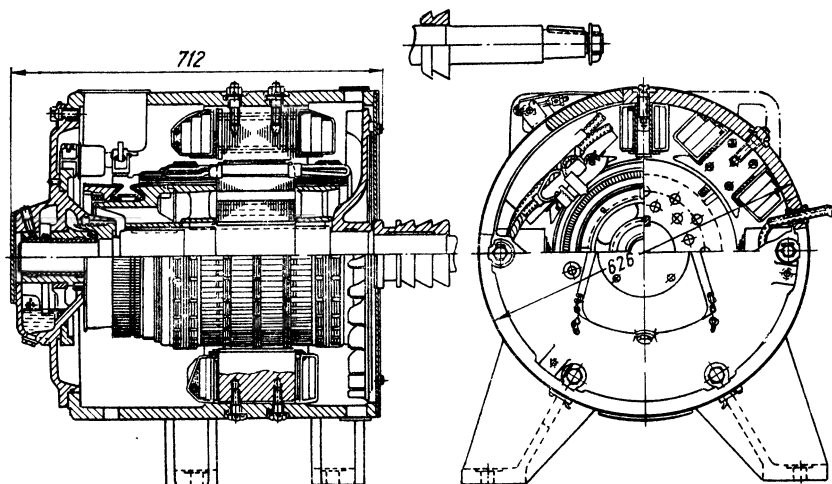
Двигатель ДК-404А компрессора Э-500
